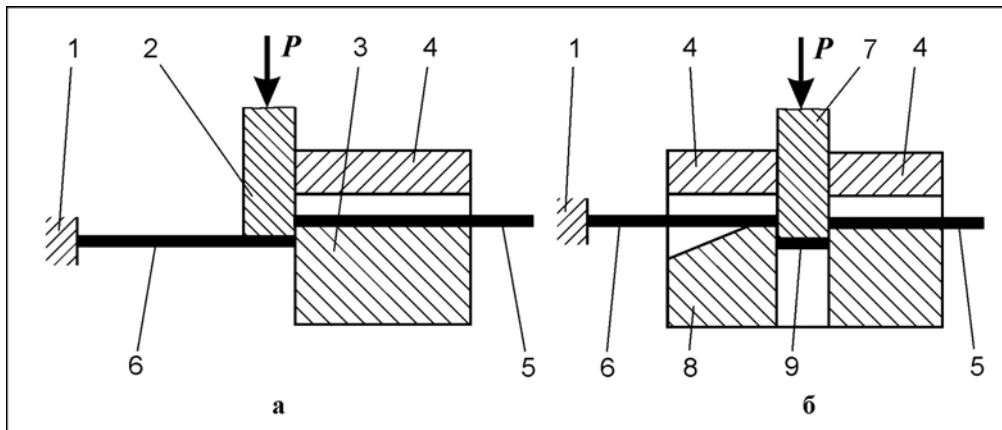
Схеми операції відрізування: а – безвідхідне відрізування; б – відрізування з відходами; 1 – передній упор; 2 – рухомий односторонній ніж; 3 – нерухомий односторонній ніж; 4 – жорсткий знімач; 5 – штаба, стрічка; 6 – заготовка, що відрізнена; 7 – рухомий двобічний ніж; 8 – нерухомий двобічний ніж (матриця); 9 – відхід
